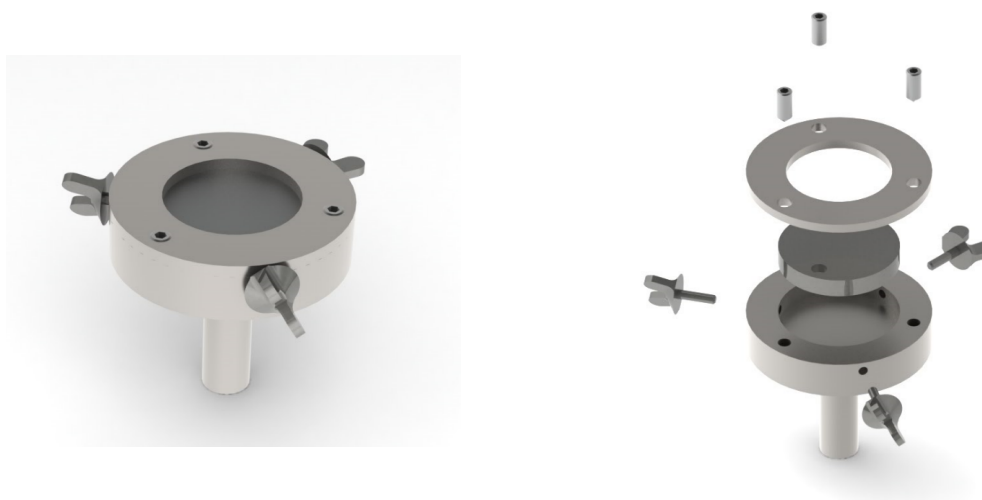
Sistema 2 - vista da montagem e vista explodida.
